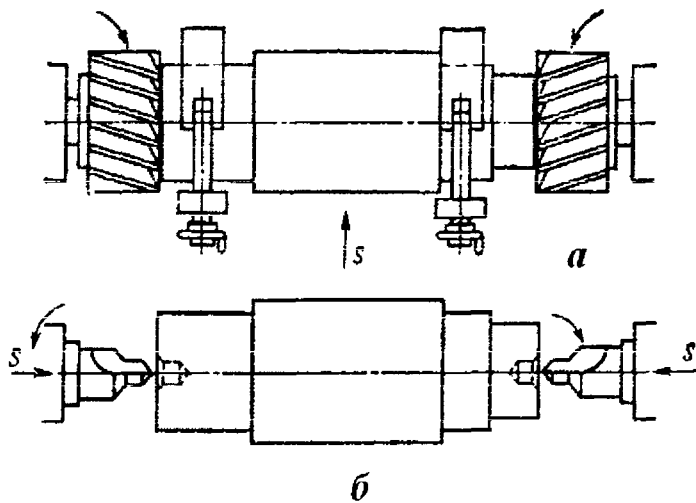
Схема обработки на фрезерно-центровальном станке
